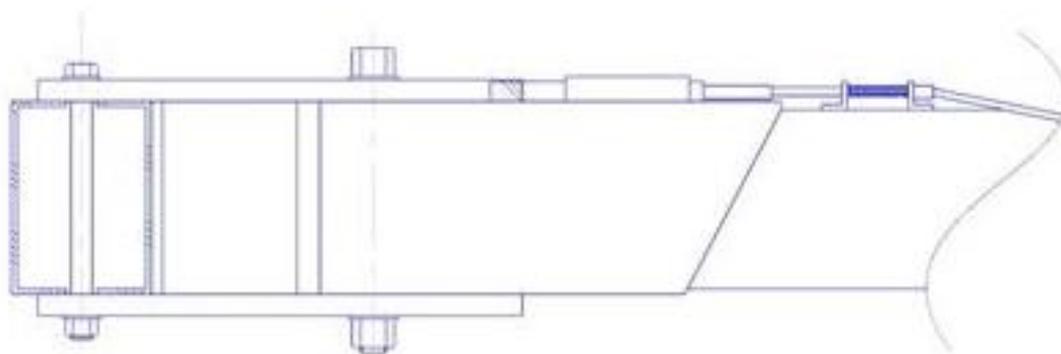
Поворотный механизм (вид сбоку)
